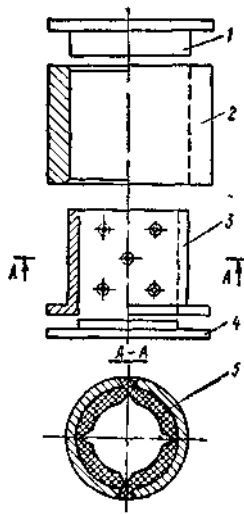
Приспособление для изготовления резине - металлического подшипника.
